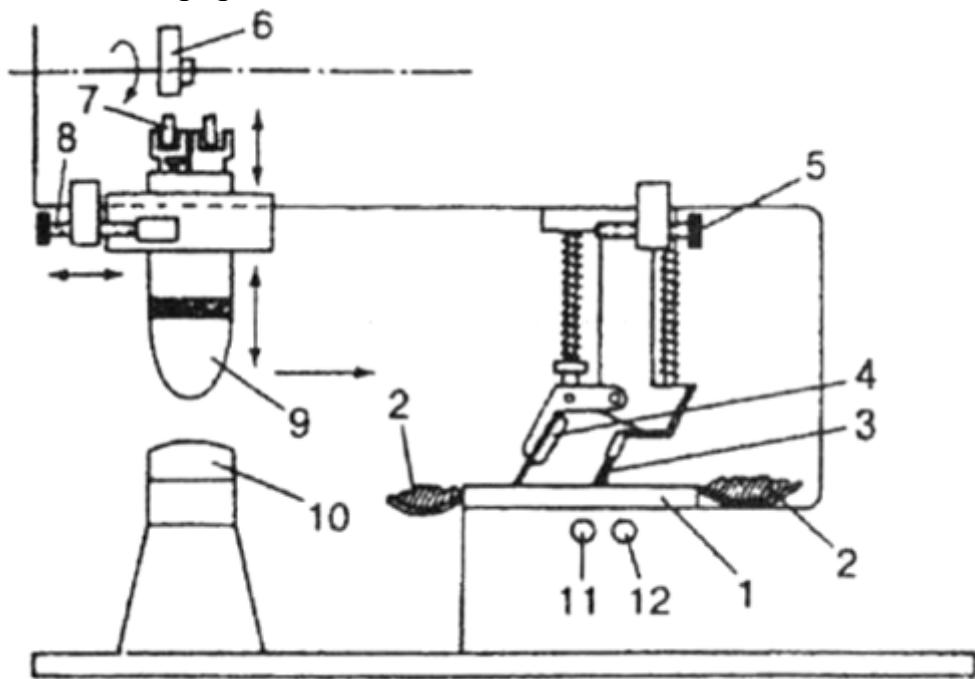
Принципиальная схема полуавтоматической печатной машины: 1 — печатная форма; 2 — резервуар с краской; 3 — краскоподающее устройство; 4 — ракельное устройство; 5 — винт регулировки перемещения ракельного механизма; 6 — устройство перемещения тампона по вертикали; 7 — регулировка перемещения тампона по вертикали; 9 — тампон; 10 — запечатываемое изделие; 11 — винт угловой регулировки положения печатной формы; 12 — винт регулировки положения печатной формы по двум координатам
